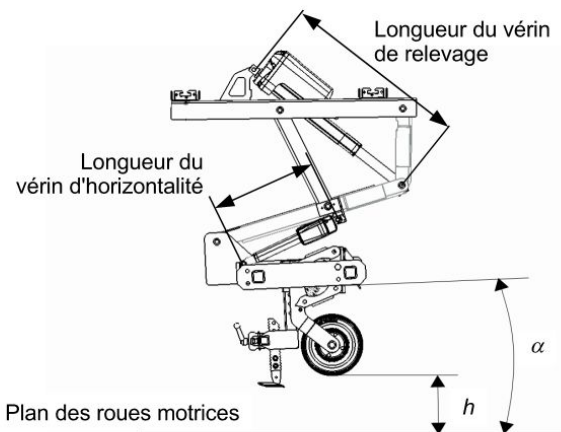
réglage du porte-outils par rapport au plan des roues motrices
